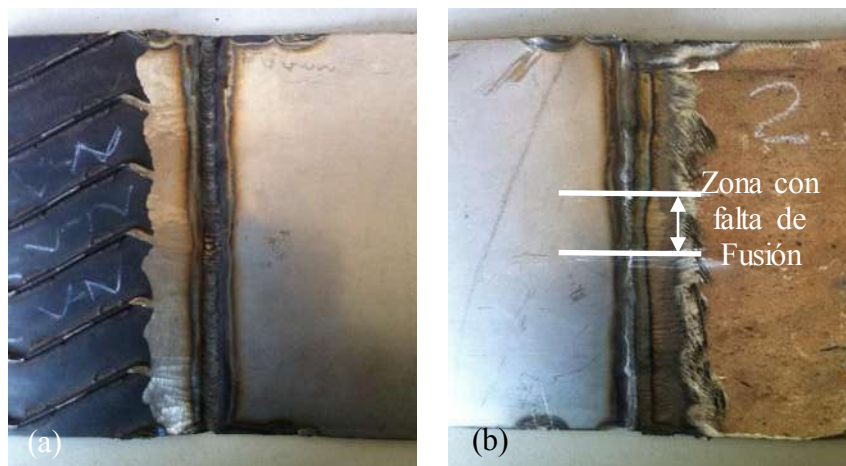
Cara de la soldadura y pasada de raíz en la unión soldada tipo C.
